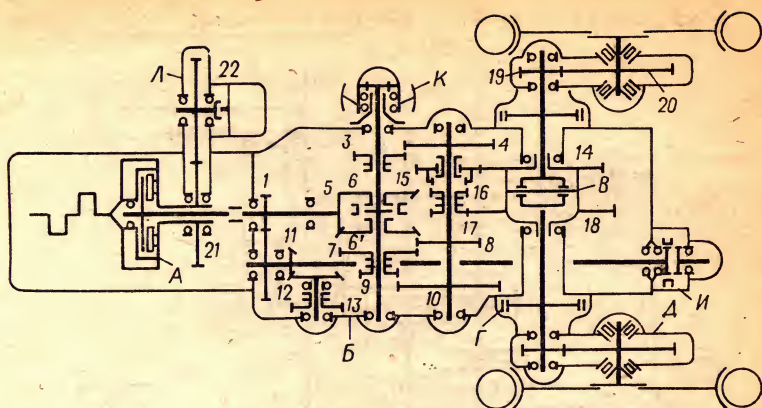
Кинематическая схема силовой передачи трактора Т-25: А — муфта сцепления; Б — коробка передач; В — центральная передача с дифференциалом; Г — ленточный тормоз; Д — конечная передача; И — зубчатая муфта включения ВОМ; К — шкив; Л — привод к насосу гидравлической системы
